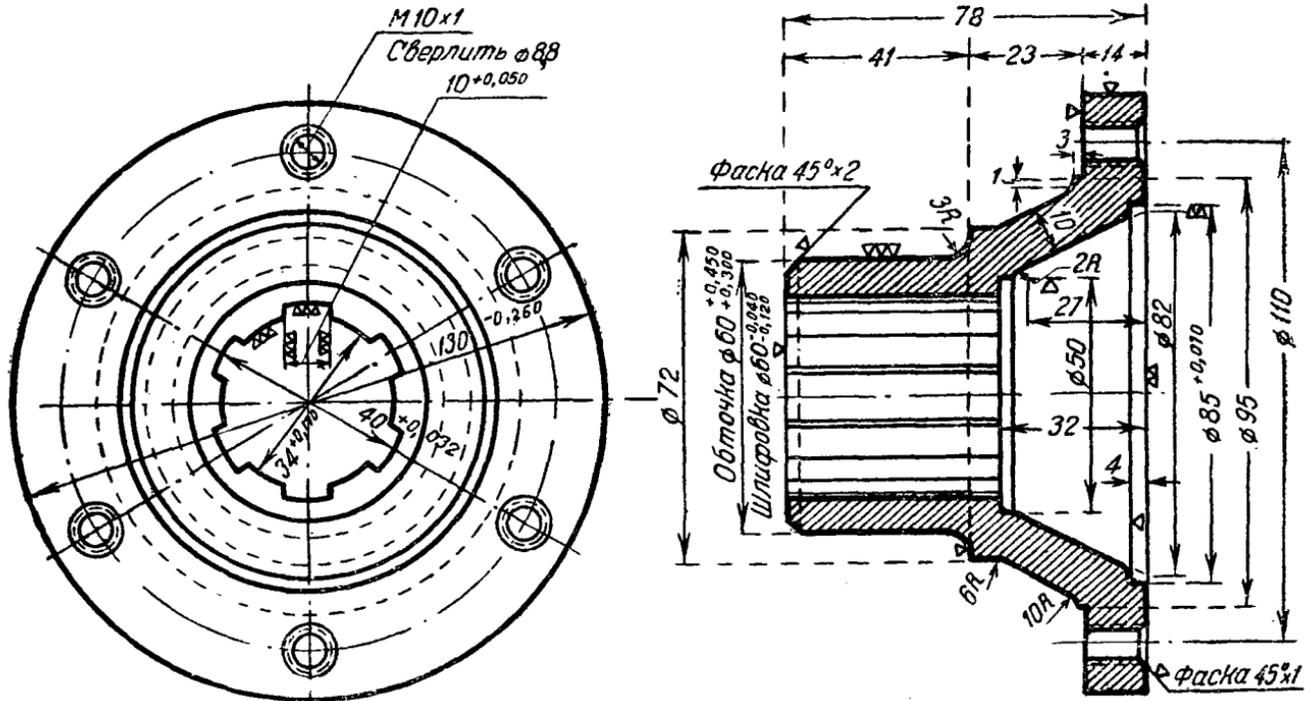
Дет. 90. Соединительный фланец валика коробки скоростей]
